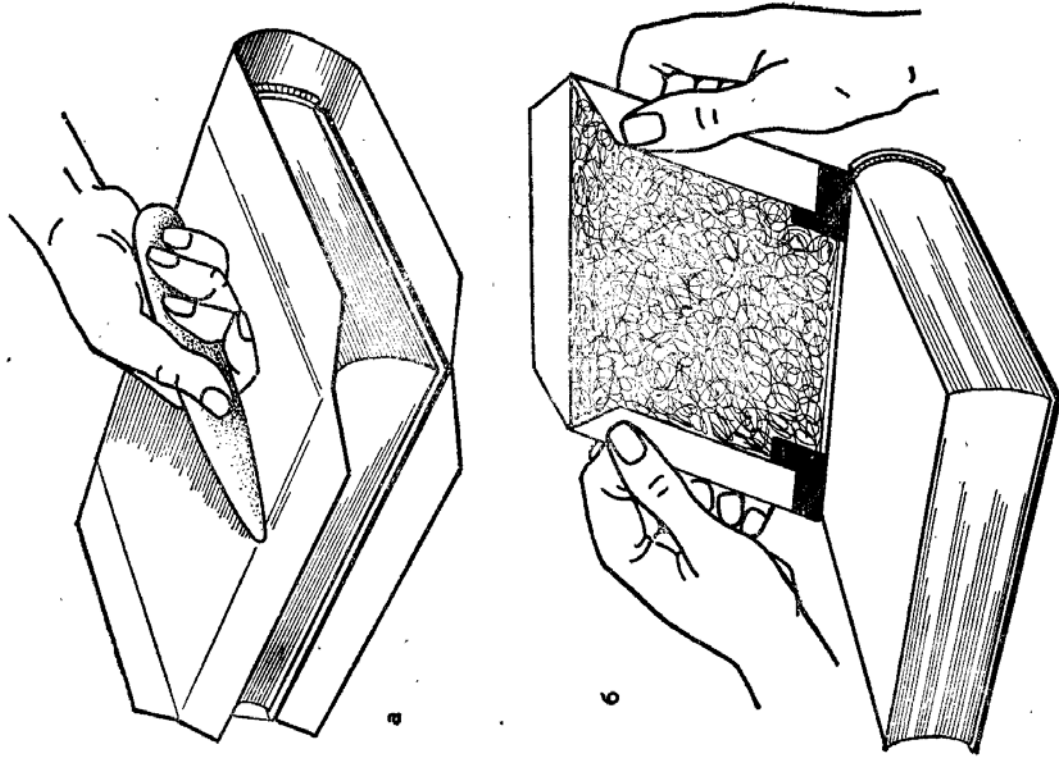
Оклеивка крышки: а — наклейка покровного материала; б — заправка кромки
